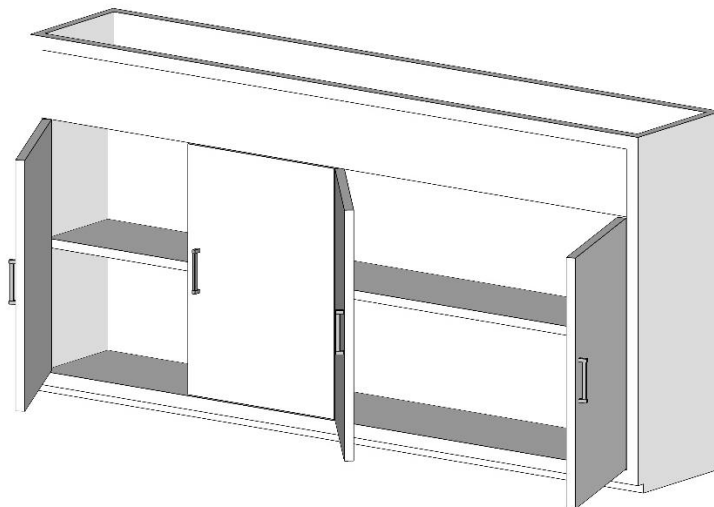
Móvel de apoio às secretárias para arquivo essencial (3). Fonte: Autor.
